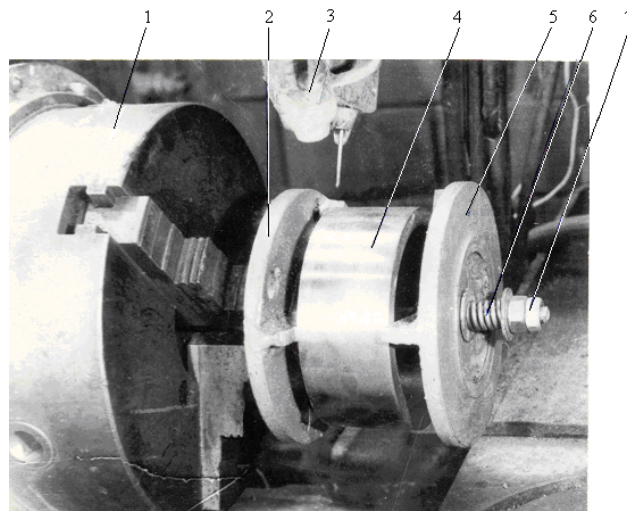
Пристосування для закріплення порожнистих циліндричних деталей при їх напавленні: 1 – патрон наплавлювальної установки; 2 – нерухомий відносно патрона фланець; 3 – газоелектричний пальник; 4 – деталь, що підлягає напавленню; 5 – рухомий фланець; 6 – пружина; 7 – різьбове з'єднання.
